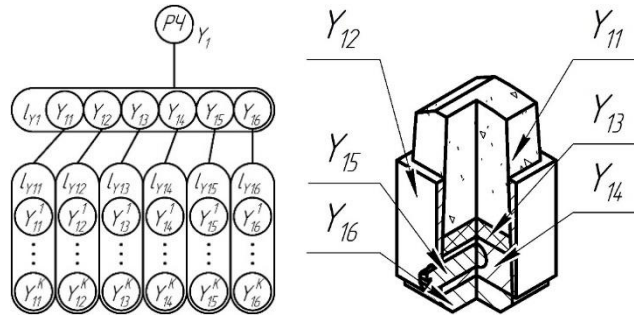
Ребро описывающее рабочую часть сборного шлифовального инструмента
